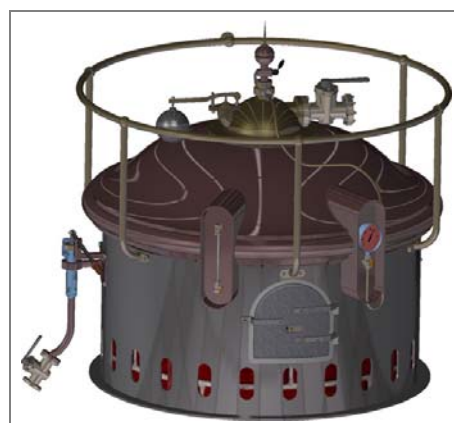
CANOT A VAPEUR DE 1861, MAQUETTE CAO DE LA CHAUDIERE
